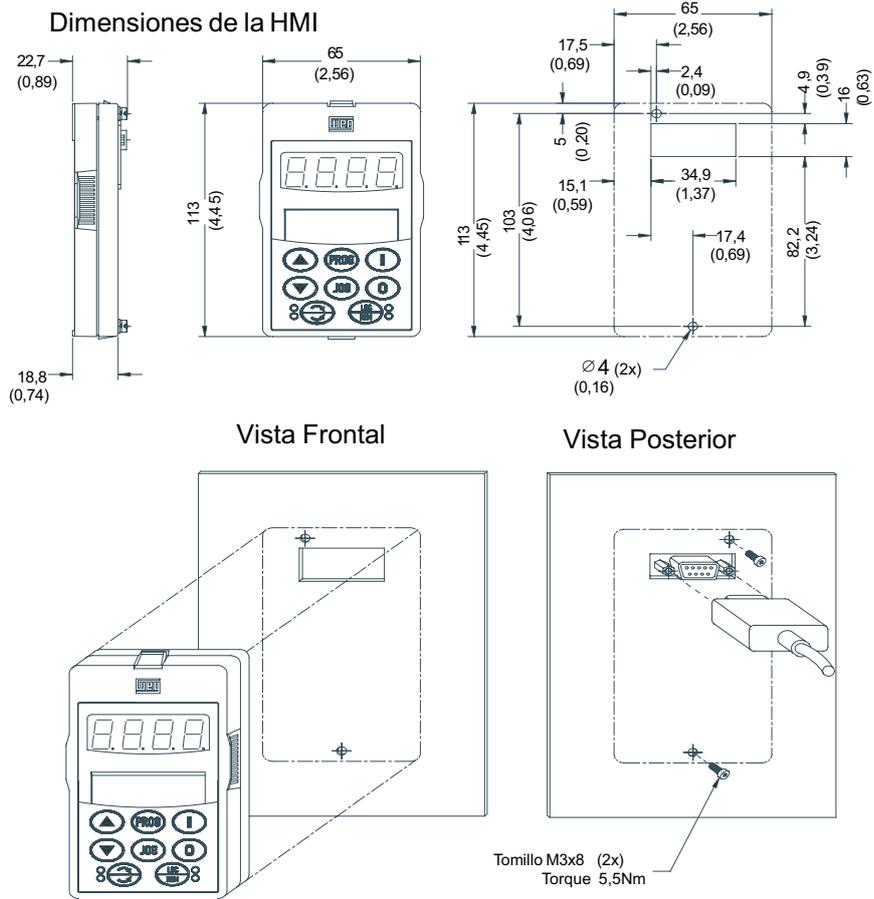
Dimensiones en mm (in) y como instalar la HMI y Moldura en el panel sen moldura
